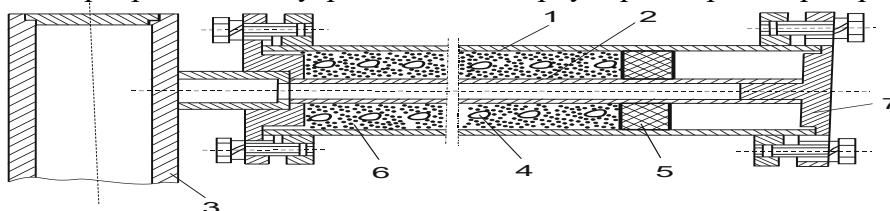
Схема конструкции реактора генератора-абсорбера с подвижным поршнем и пружиной, работающей на расширение: 1 – корпус реактора; 2 – трубка перфорированная 3 – трубка для отвода - подвода хладагента к реактору; 4 – пружина в сорбенте; 5 – поршень; 6 – сорбент; 7 – крышка реактора
